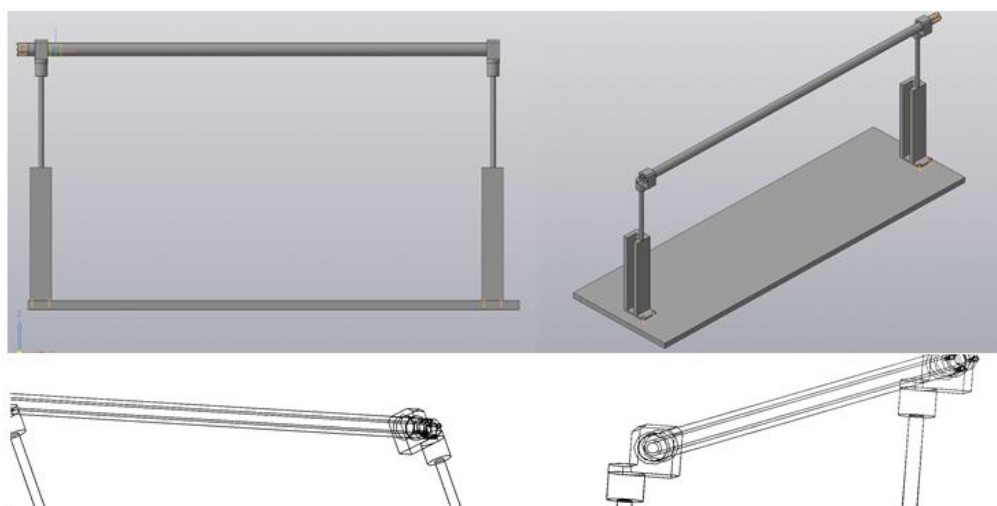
Фрагменты сборки направляющей трубы и внутренней трубы из полиамида
